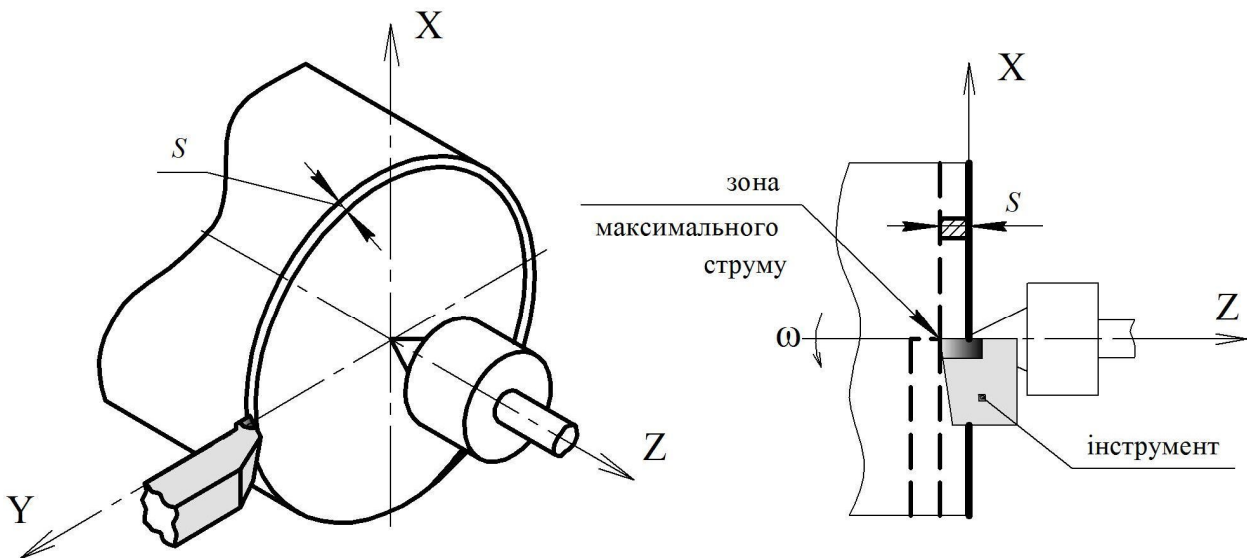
Моделювання фізичного процесу зрізання кільця із заготовки
